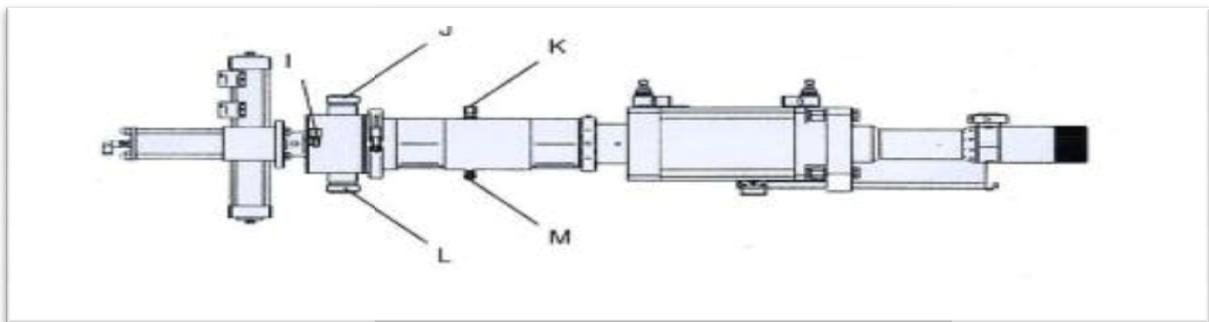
Vue de l'arrière (avec rotation) [5]
